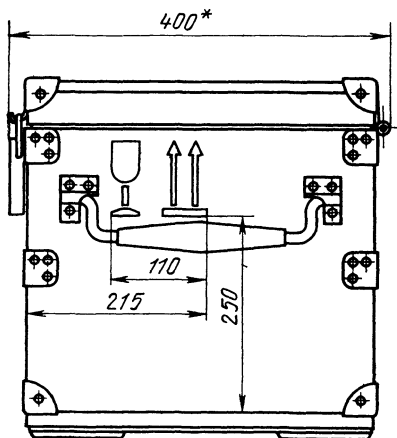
Сборочный чертеж упаковки по варианту А, лист 1
